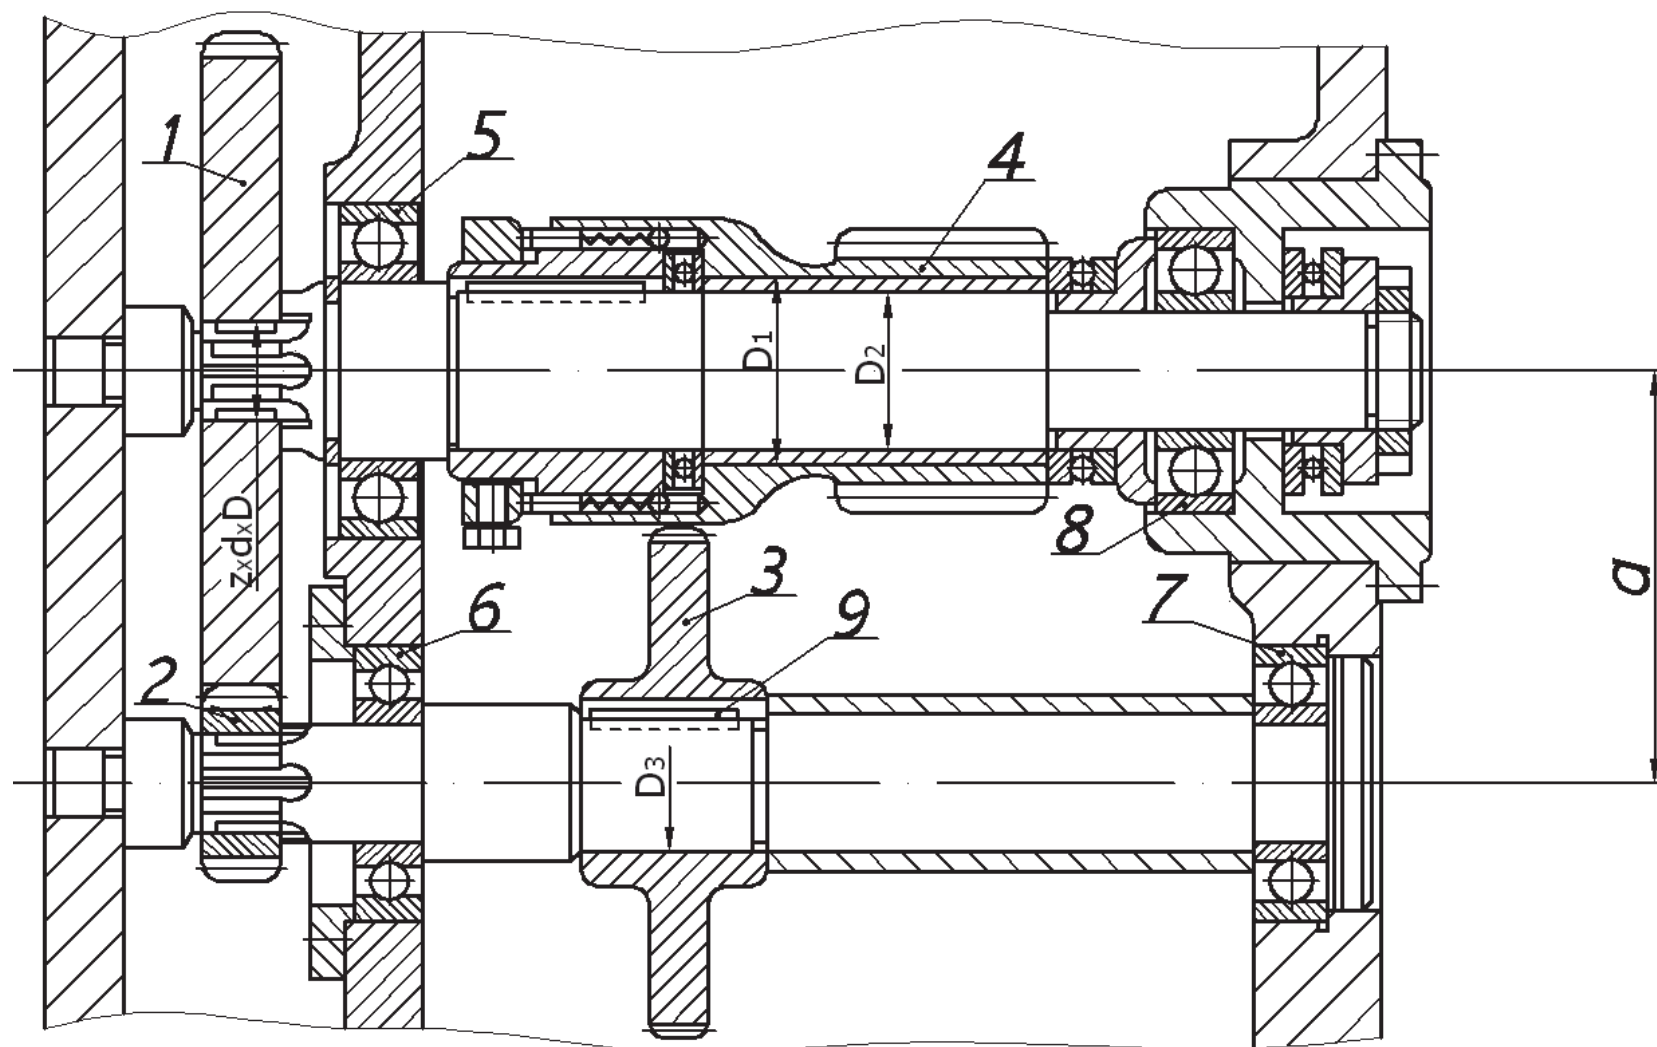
Часть механизма подачи металлорежущего станка (варианты 61-75)
